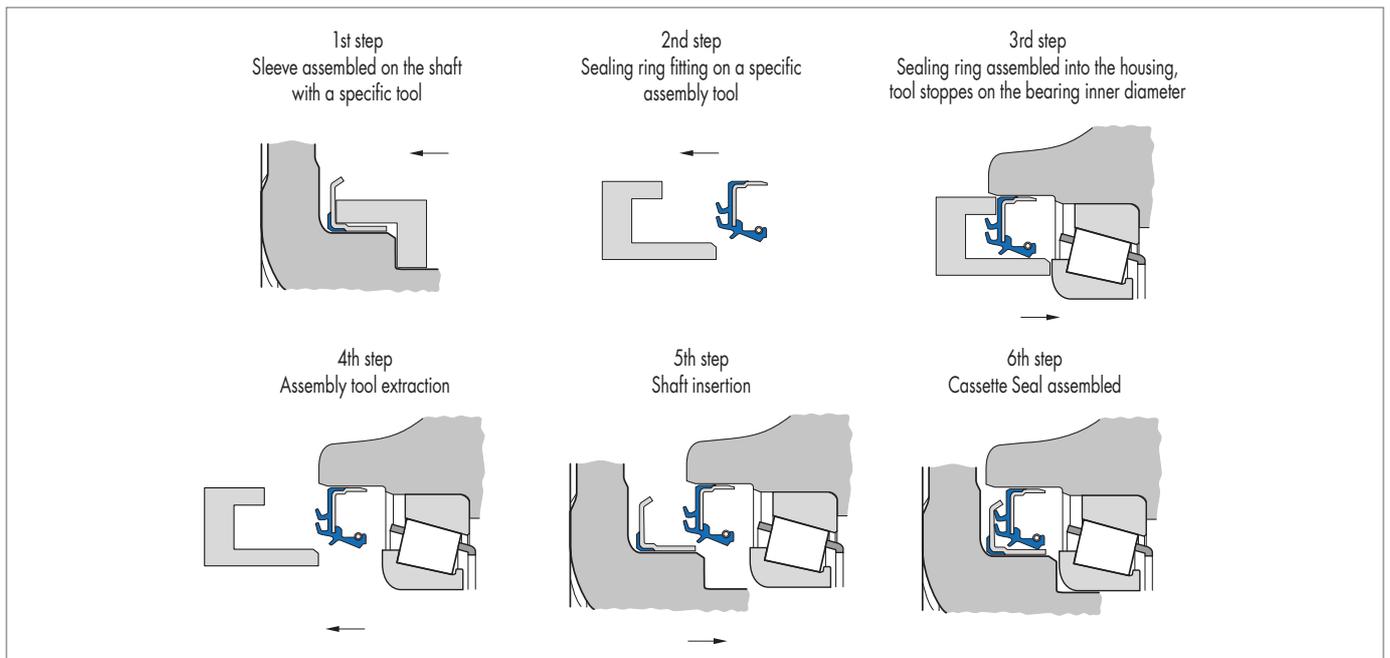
Montage Fall E („2-Phasen-Montage“) für Sonderbauformen in geteilter Ausführung / Montaj durumu E („2 adımda montaj“) iki parçalı tasarım için özel tasarımlar / Przykład instalacji E ("Montaż 2-stopniowy") dla wersji specjalnych w splicie realizacji / Пример монтажа E («2-х ступенчатая сборка») для особых форм строительства в разделенном исполнении
